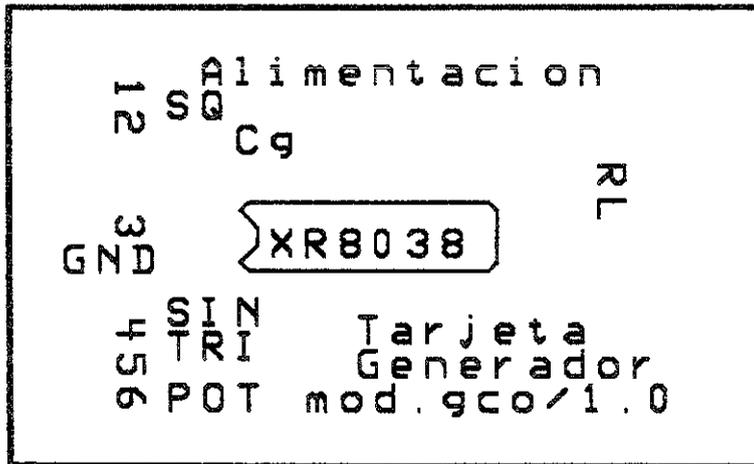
Dibujo del circuito impreso de la tarjeta del generador. Lado de los componentes
